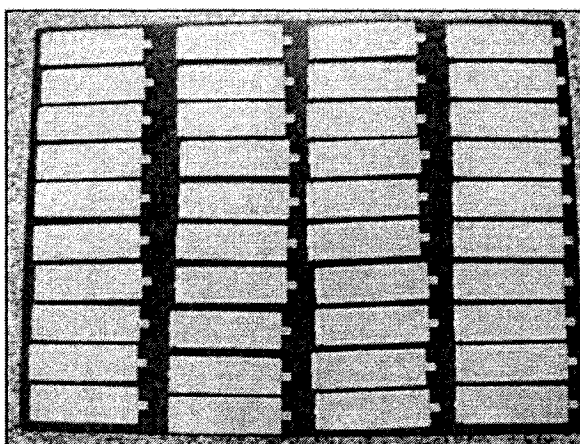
Éprouvettes mises sur une surface plate après avoir été moulées.
